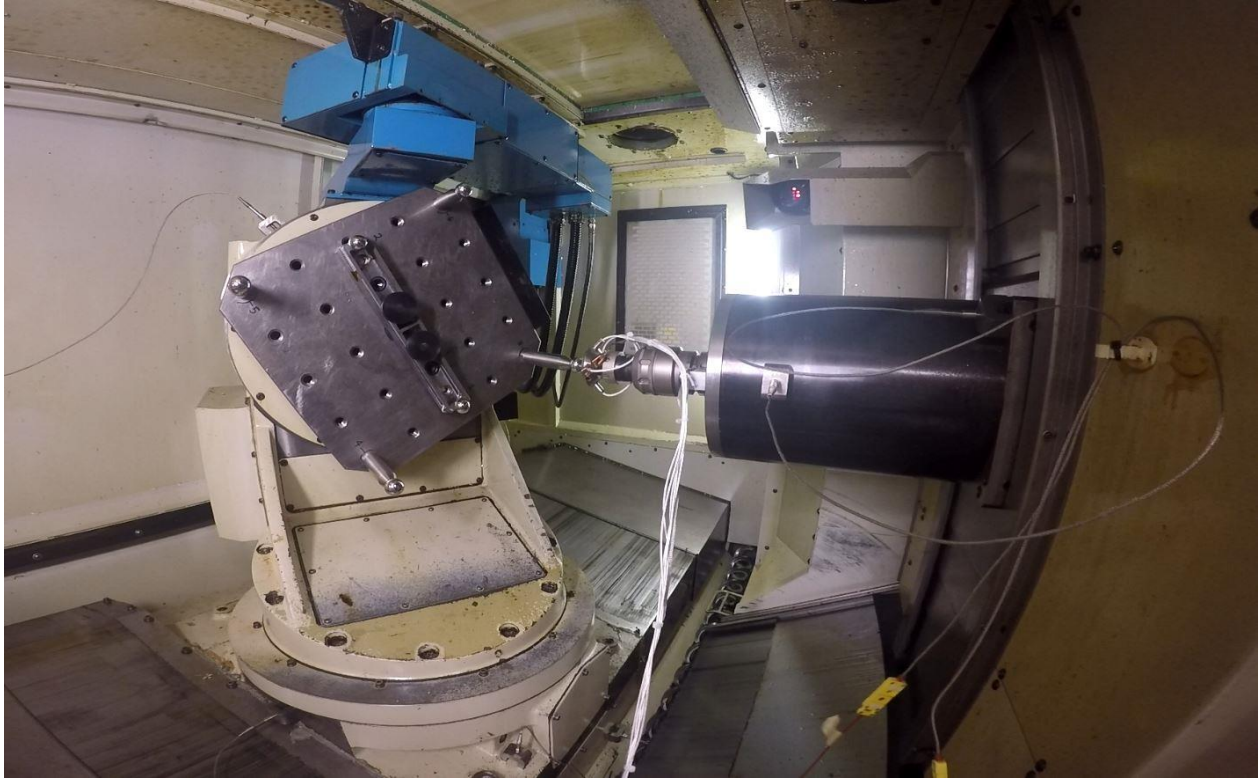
Montage expérimental sur la machine-outil HU40-T
